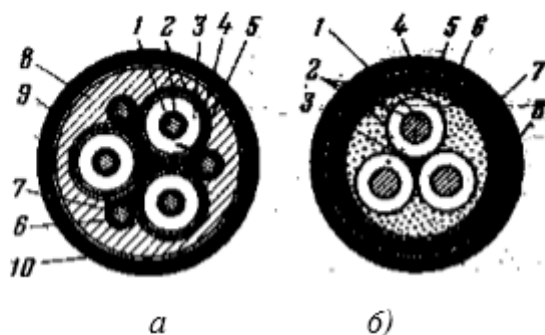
Конструкции немецких кабелей. а-экскаваторного типа NTSCE: 1 - токопроводящая жила; 2 - слой проводящей резины; 3-изоляция; 4 -озоностойкий слой; 5 -обмотка тканевой лентой; 6 - сердечник из проводящей резины; 7 -заземляющая жила, покрытая проводящей резиной; 8 - внутренняя оболочка; 9 -обмотка тканевой лентой; 10- наружная оболочка. б - шахтного фирмы «Сименс»: 1 - токопроводящая жила; 2 - слой проводящей резины; 3 - сердечник-заполнитель; 4 - обмотка тканевой лентой; 5 - металлический экран; 6 - слой изоляционной резины; 7- второй металлический экран; 8-полихлоропреновая оболочка.
